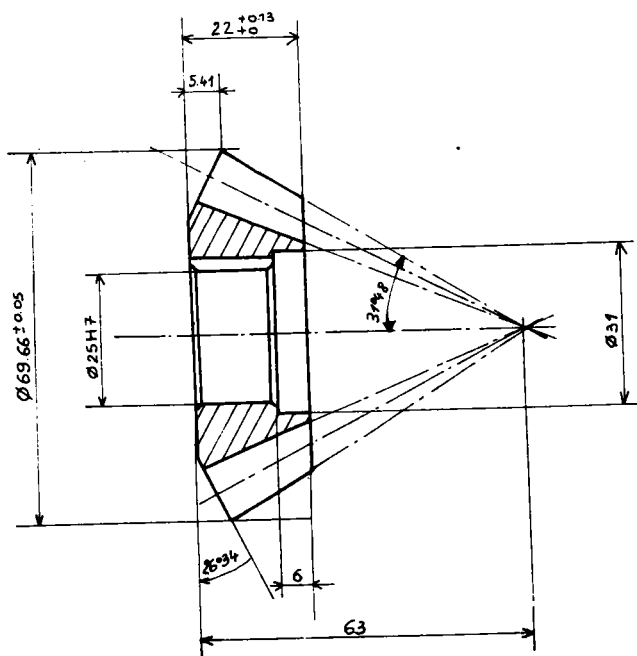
Pièce codée : N° de plan : 4052
